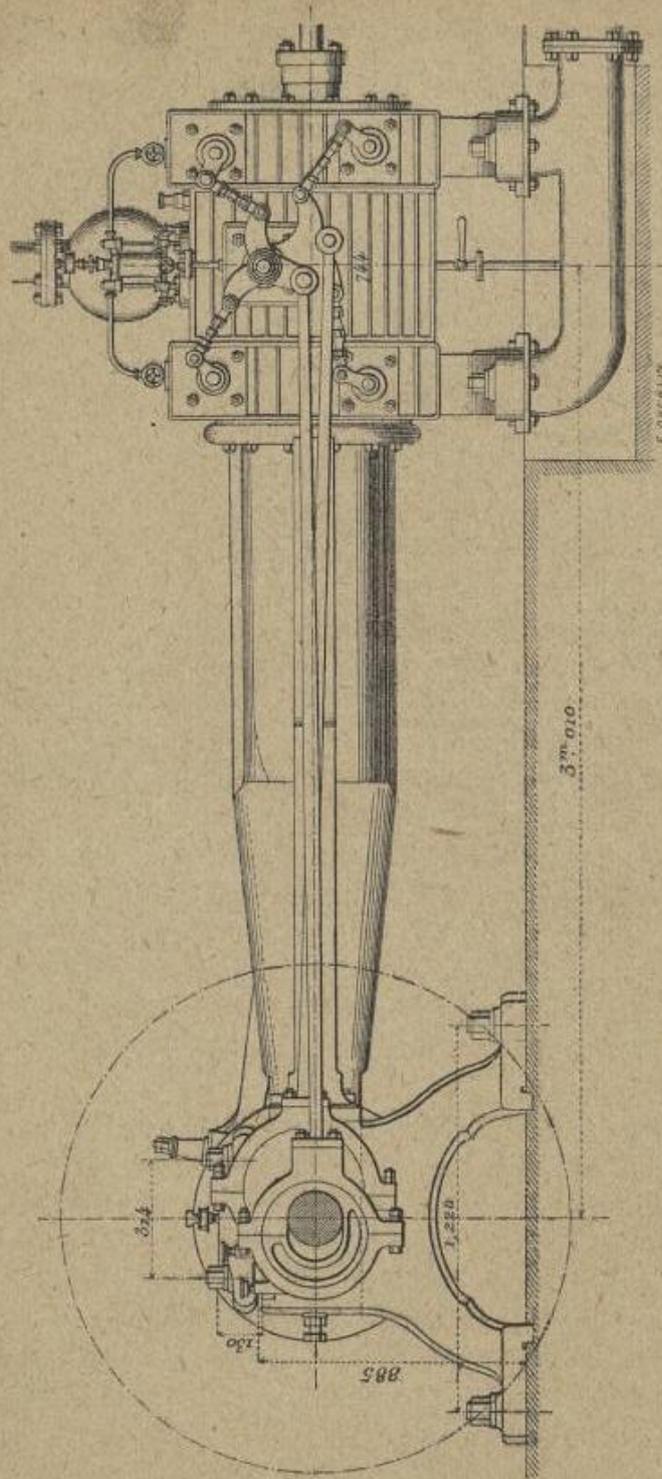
Machine rapide à quatre distributeurs sans déclenchement, construite par E. Garnier en 1889; nombre de tours par minute, 180; régulateur de Porter, non représenté sur la figure, agissant sur une soupape placée à l'arrivée de vapeur; excentrique à calage variable commandant les distributeurs d'admission; excentrique à calage fixe pour les distributeurs d'échappement.
